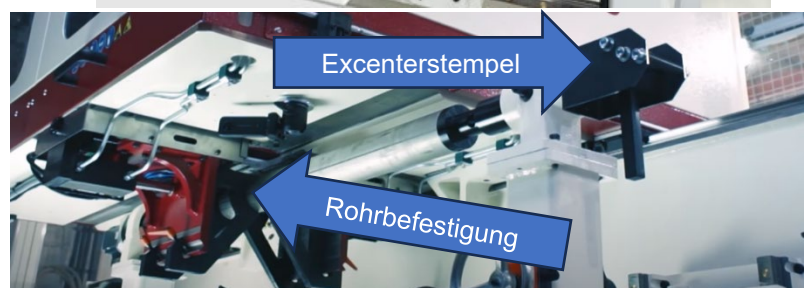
/ Detail 4 zu T-Drill SEC-115
